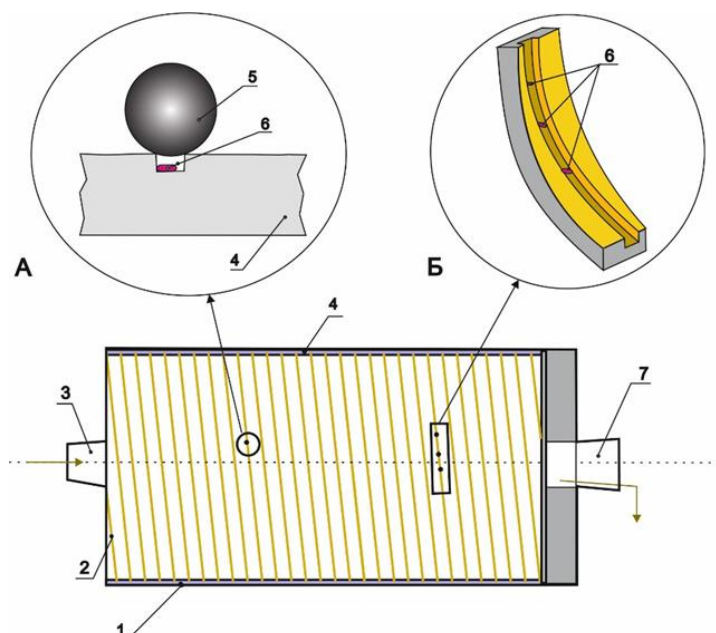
Шаровая мельница с постоянной разгрузкой полезного компонента: 1 – барабан; 2 – рифли; 3 – загрузочный патрубок, 4 – броня, 5 – мелющий орган, 6 – полезный компонент, 7 – разгрузочный
